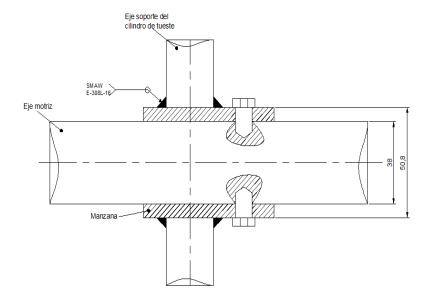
Junta soldada eje soporte y manzana del eje motriz
